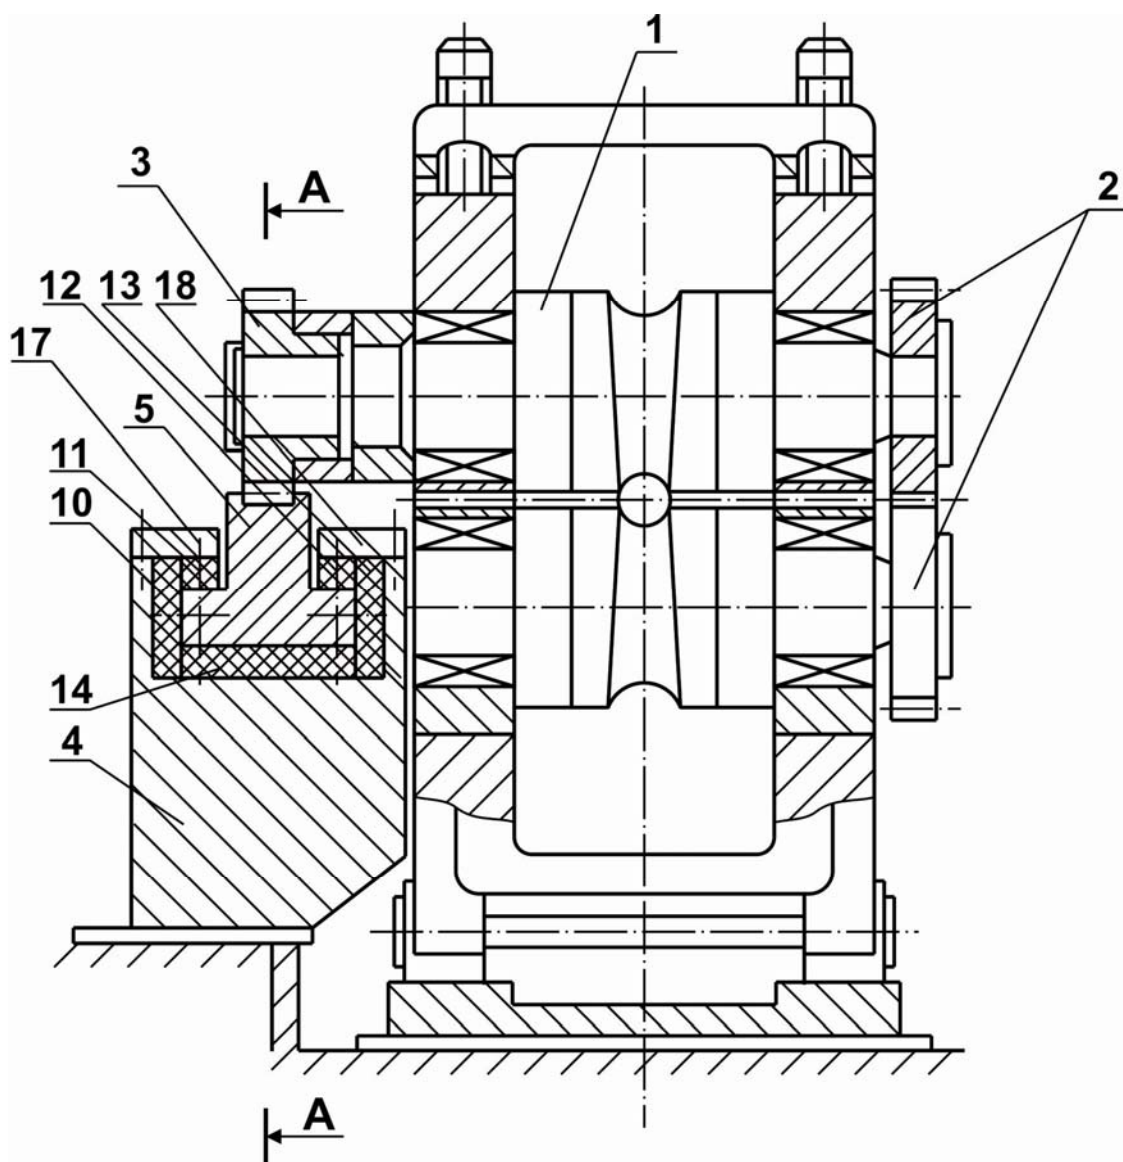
Подвижная клеть стана ХПТ с новой конструкцией привода валков
